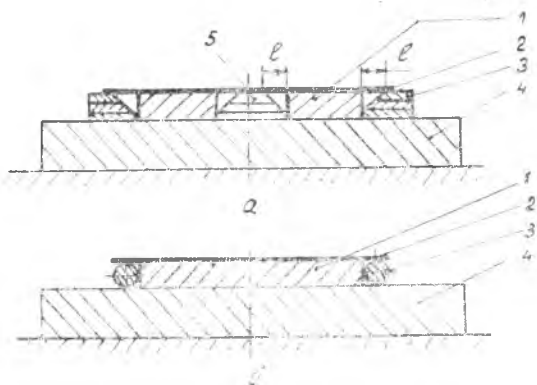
Схема вырезки полиуретаном деталей на вырезных шаблонах с опорными вкладышами и рамкой, набранной из пластин (а) и изготовленной из проволоки (б): 1 — вырезной шаблон; 2 — заготовка; 3 — опорная рамка; 4 — подштамповая плита; 5 — вкладыш
